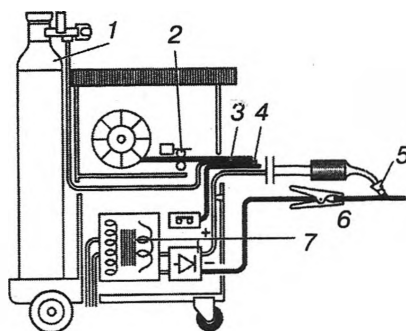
Установка для напівавтоматичного зварювання в захисному газі плавким електродом:
